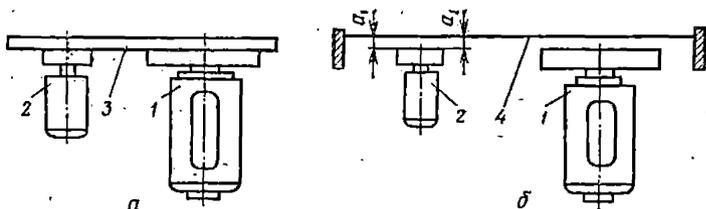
Приспособление для проверки параллельности торцевых частей шкива и маховика при ременной передаче:
